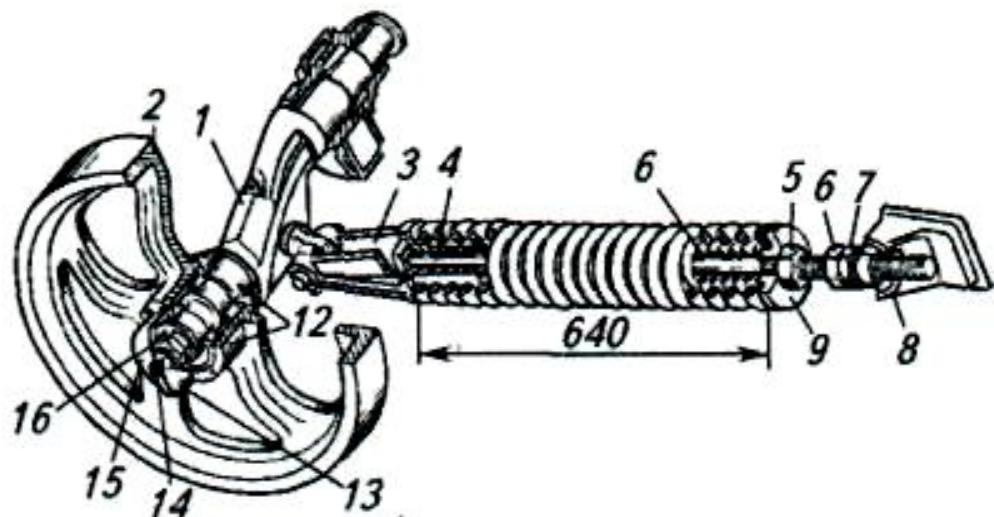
Натяжное устройство трактора с балансирной подвеской
